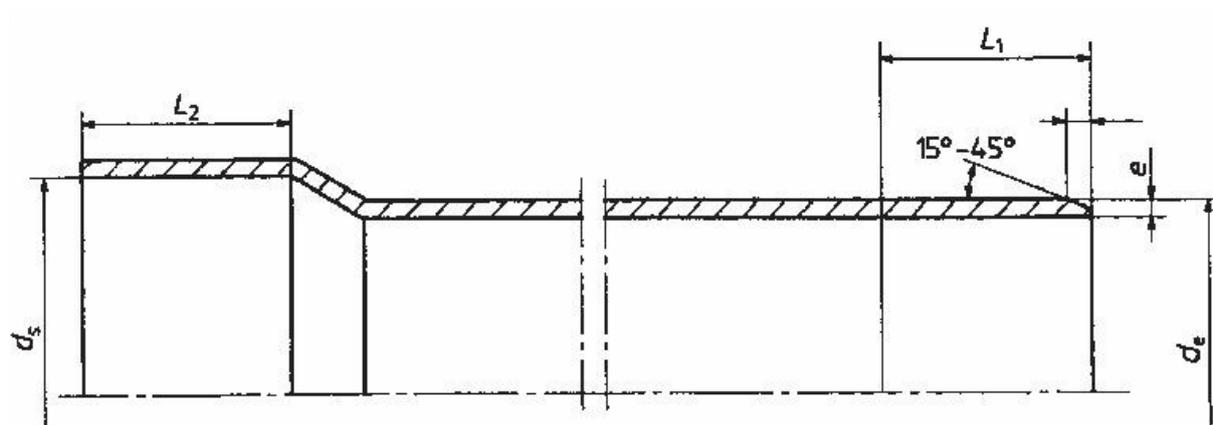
Dimensiones básicas de embocaduras para unión por encolado
